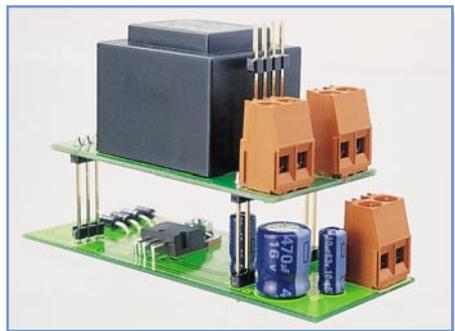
Die komplett montierte FS20-ESH-Baugruppe
